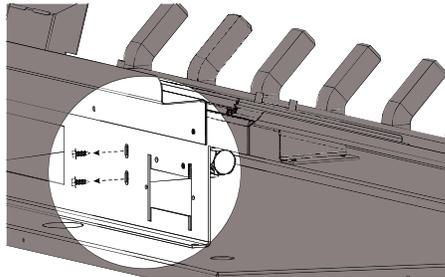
Vue de Côté/Arrière de l'Assemblage de Soupape
